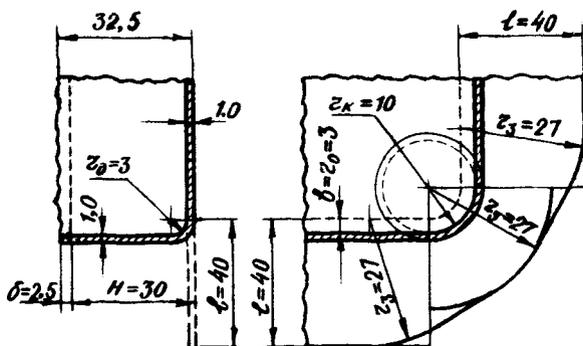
Схема построения контура заготовки для прямоугольной детали (к расчету размеров и формы заготовки)
